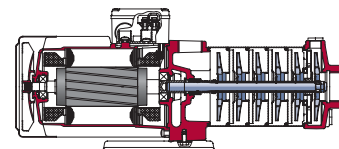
Горизонтальный консольный многоступенчатый насос
